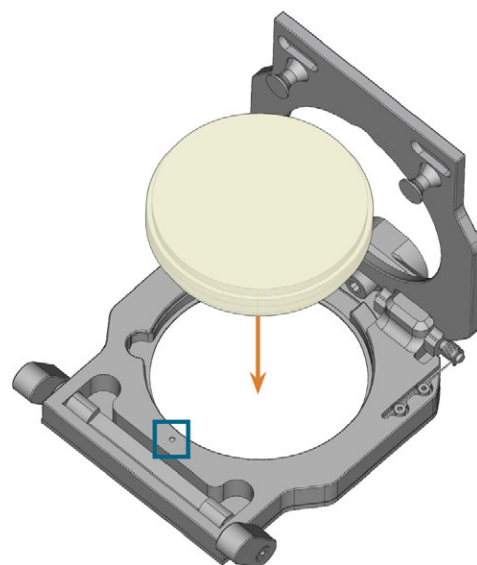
INSERTION D'UN DISQUE DANS LE PORTE-PIÈCE (POSITION POUR REMONTAGE SÛR MARQUÉE EN BLEU)
